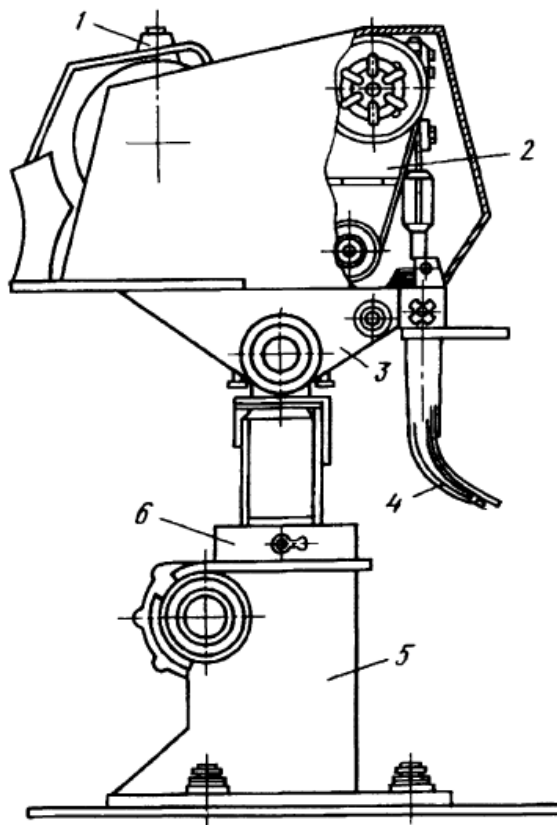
Схема вибродуговой установки ОКС-6569: 1 – электродвигатель; 2 – механизм подачи проволоки; 3 – вибратор; 4 – мундштук для подвода проволоки к детали; 5 – опорный узел; 6 – механизм подъема
